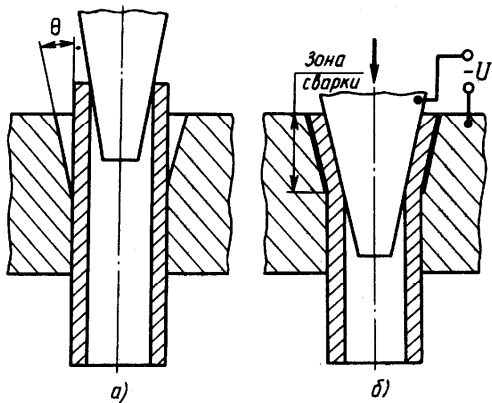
Электроконтактная сварка сопротивлением труб с трубной доской
